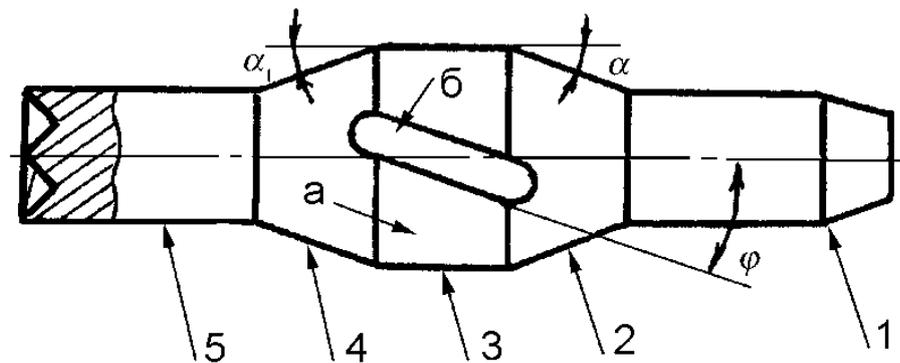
Конструктивная схема дорна: 1 — направляющая часть; 2 — заходной (заборный) конус; 3 — калибрующая часть; 4 — задний конус; 5 — хвостовик; а — выступ; б — впадина
